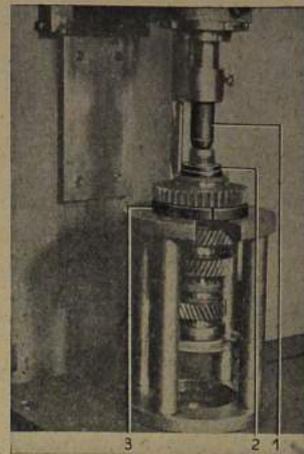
Inneren Laufring für Zylinderrollenlager abpressen
